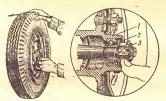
Регулировка подшинников ступицы переднего колеса: I — ступица; 2 — шайба; 3 — гайка.
